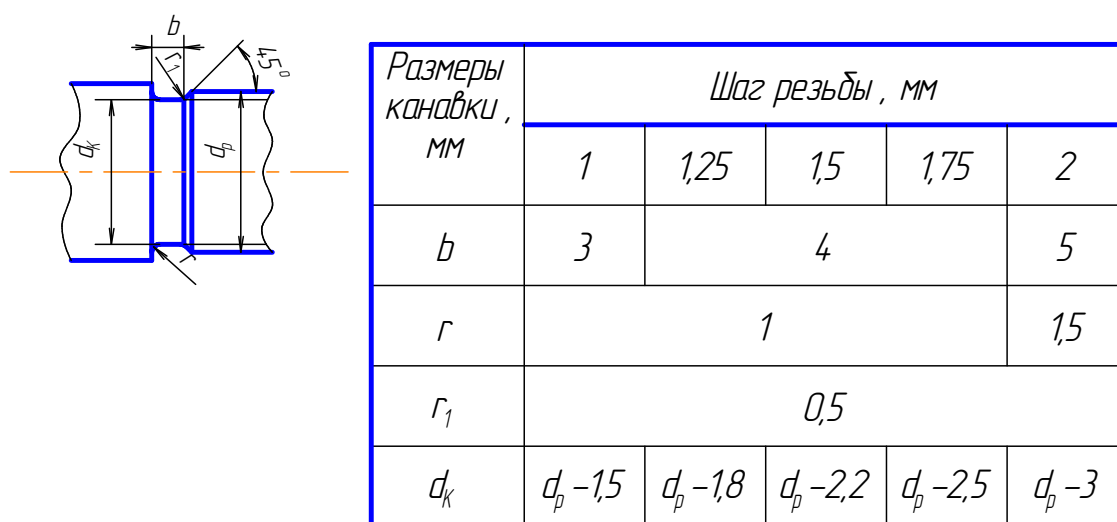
Канавки для выхода резьбонарезного инструмента
